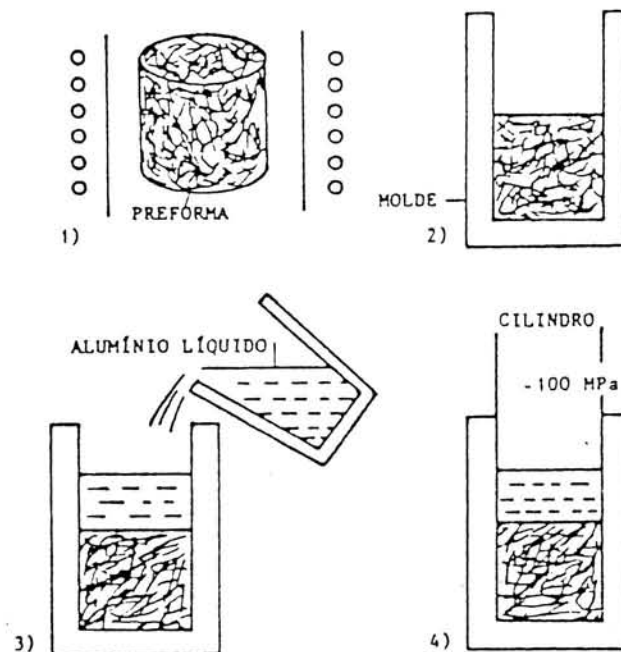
Princípio básico da infiltração sob elevada pressão [5]
